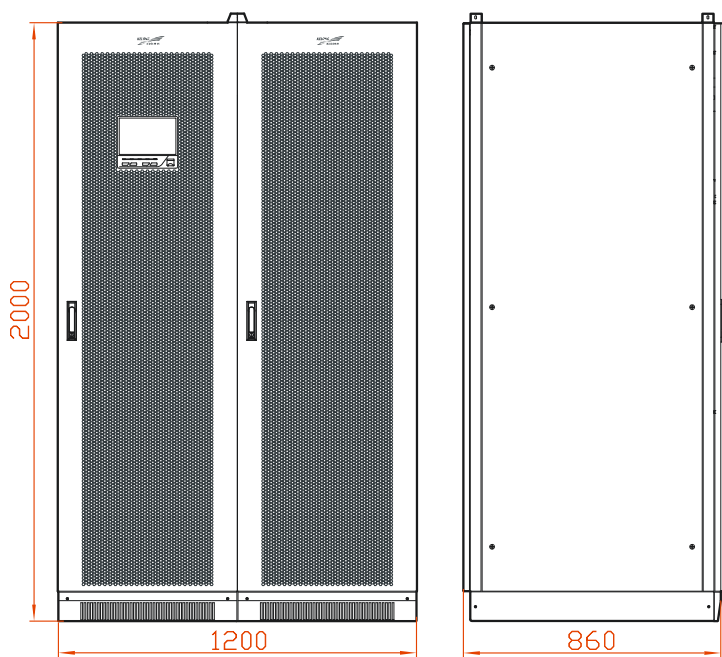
Размеры MR33400, MR33500, MR33600
